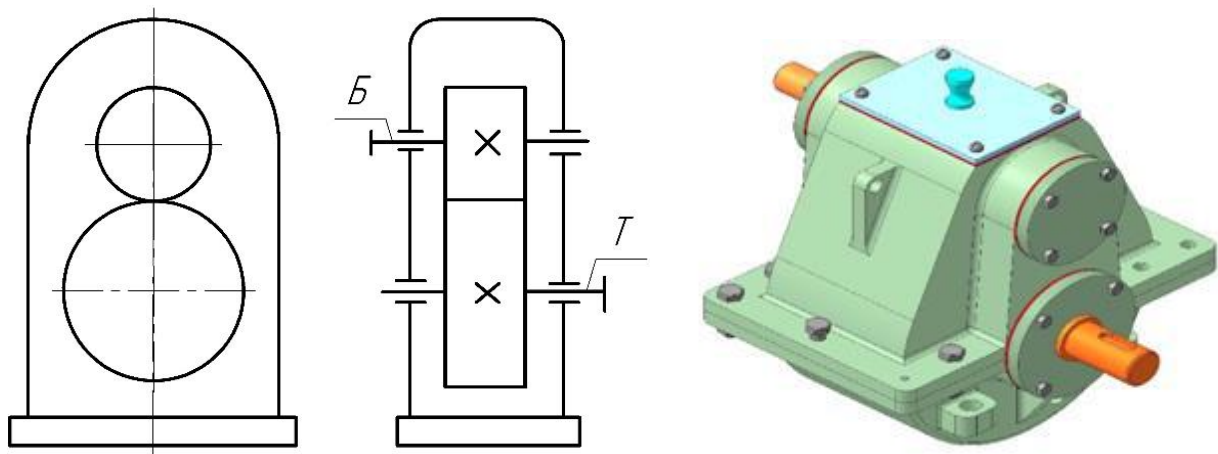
Одноступенчатый вертикальный редуктор
